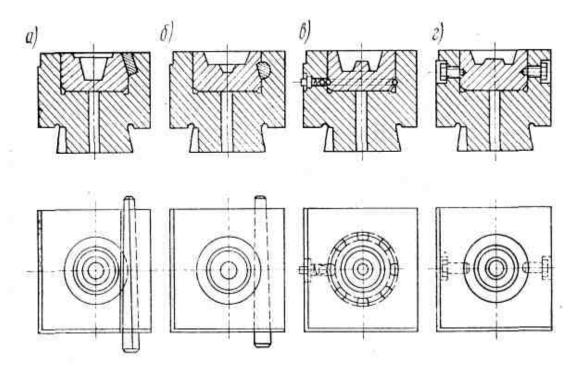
Схема крепления сборных молотовых штампов: а – призматическими клиньями; б – цилиндрическими клиньями; в – шариковое; г – винтами
